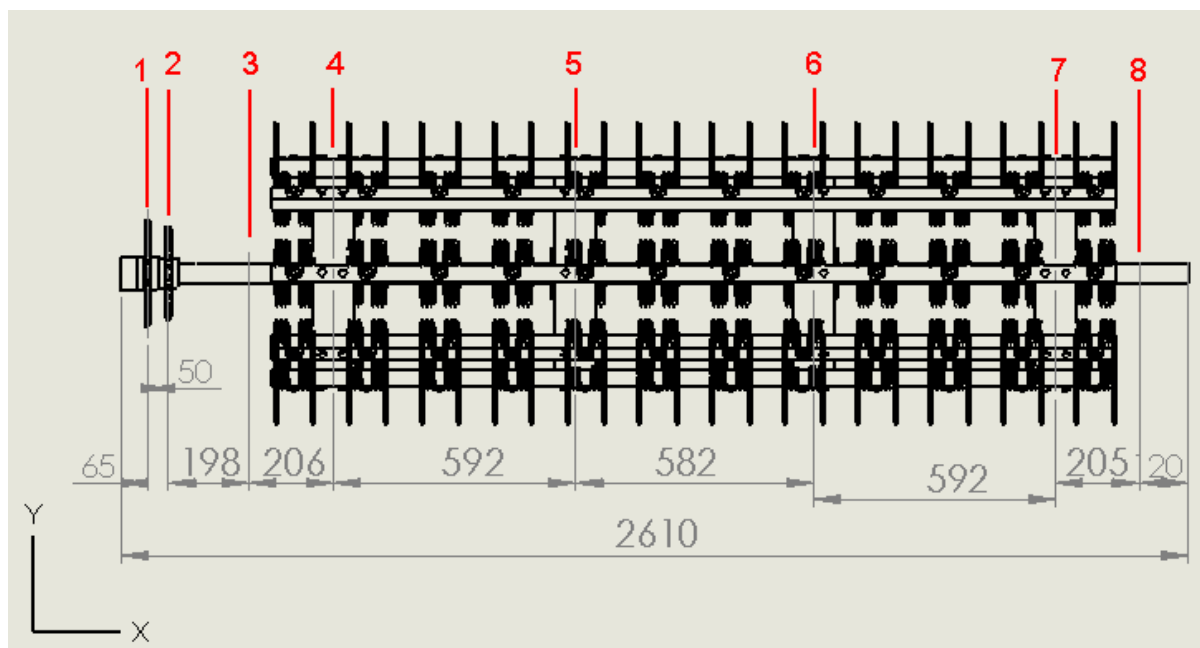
Vista frontal de elementos principales de tercer cilindro
